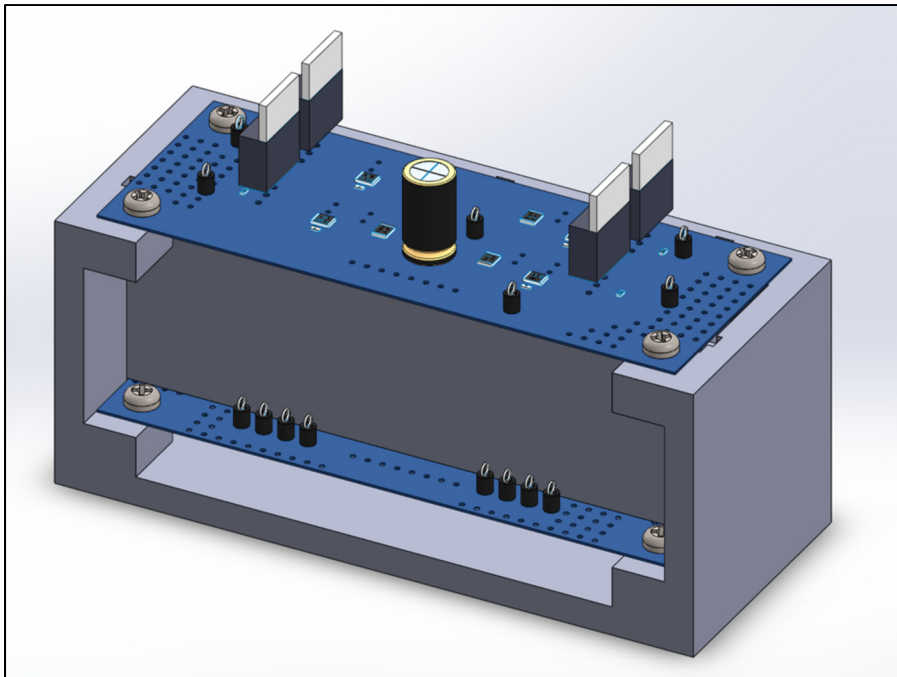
Assemblage 3D du boîtier, du mur de séparation, et des PCB de DEL et de cellules PV
